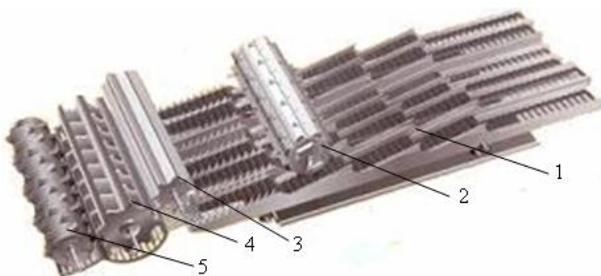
Соломотряс зерноуборочного комбайна ПАЛЕССЕ GS14:
